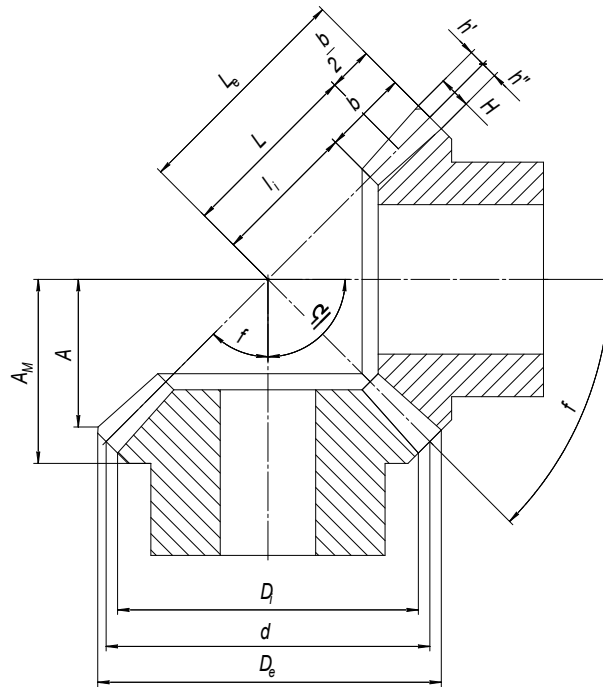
Розрахункова схема конічних зубчастих коліс
